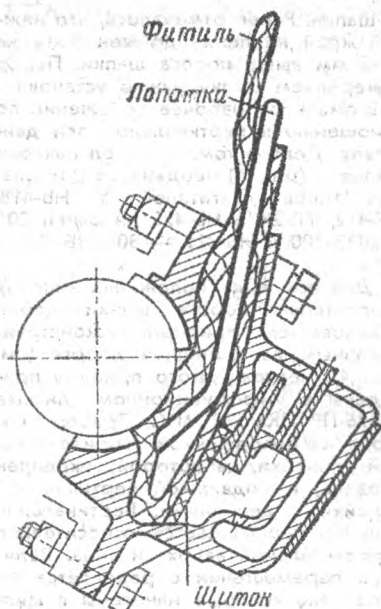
Укладка кос в шапку моторно-осевого подшипника
